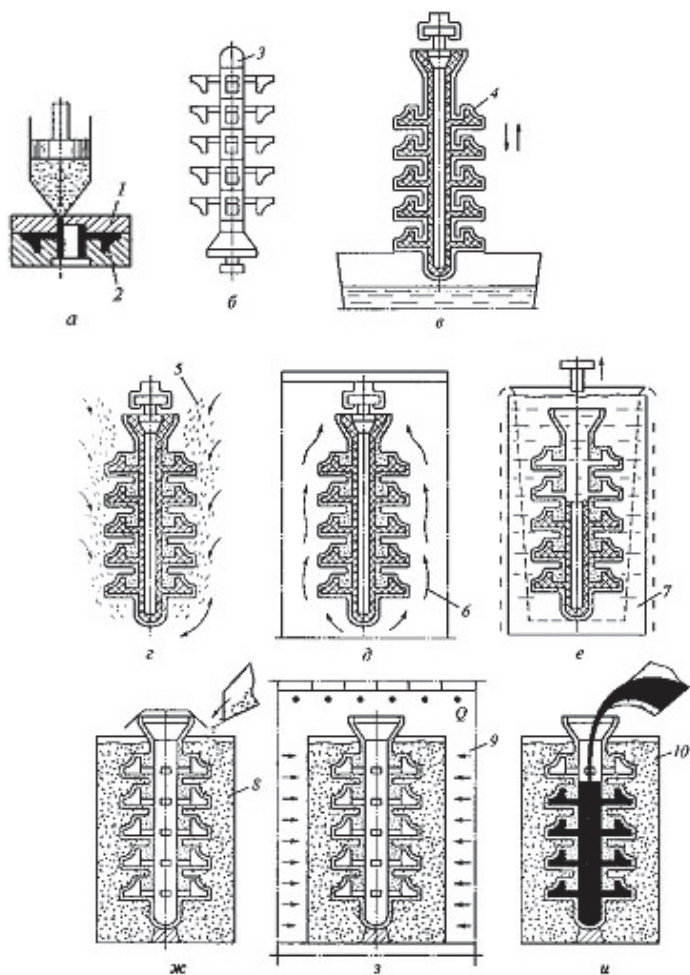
Схема изготовления тонкостенной керамической формы по выплавляемой модели: а — запрессовка модельного состава в пресс-форму; б — сборка блока; в — нанесение на блок суспензии; г — посыпка огнеупорным зернистым материалом; д — сушка; е — удаление модели; ж — засыпка огнеупорным материалом; з — прокатывание в печи; и — заливка расплавом; 1 — пресс-форма; 2 — модель; 3 — блок моделей отливок и литниковой системы; 4 — слой суспензии; 5 — огнеупорный зернистый материал; 6 — пары аммиака; 7 — горячая вода; 8 — металлический контейнер; 9 — опорный материал; 10 — печь для прокатки формы
